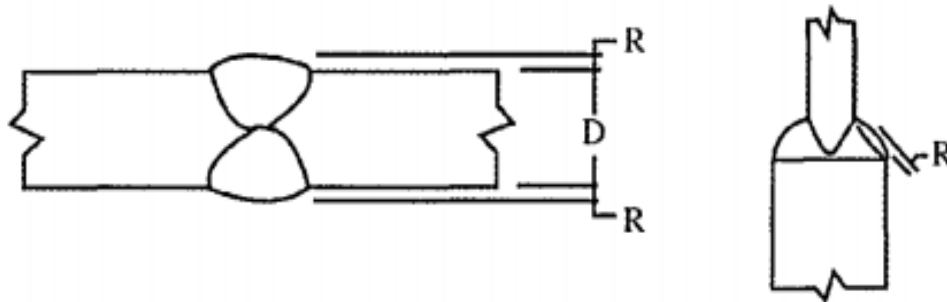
88 Perfil aceptable de soldadura de ranura.
